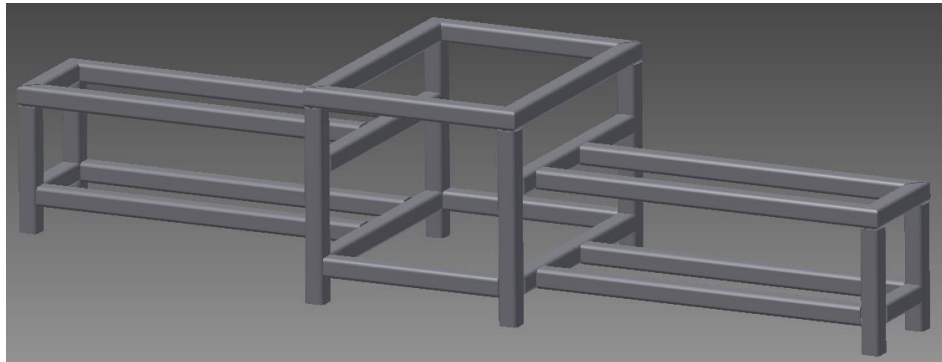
ENSAMBLE CÁMARA DE CORTE Y TAMIZ.
